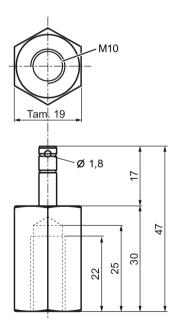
Desenho de dimensões do suporte de substituição rápida 6GT2690-0AH10
